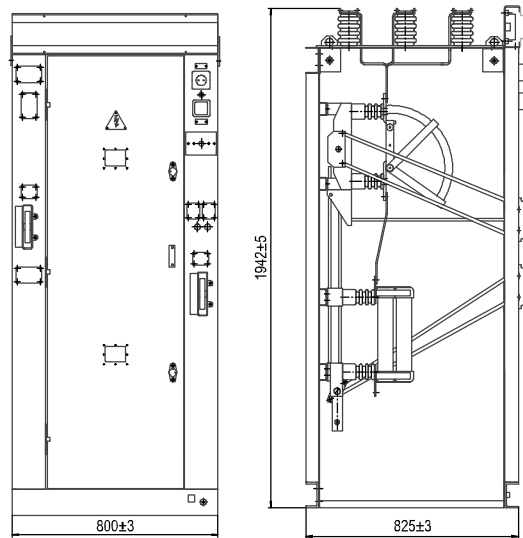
Габаритные, установочные, присоединительные размеры КСО-306 с автогазовым выключателем нагрузки ВНП-М1-10/630.
